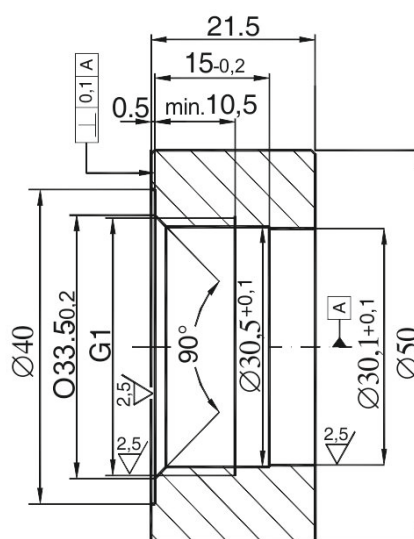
ф. Монтажное кольцо под сварку для присоединения типа CG1
